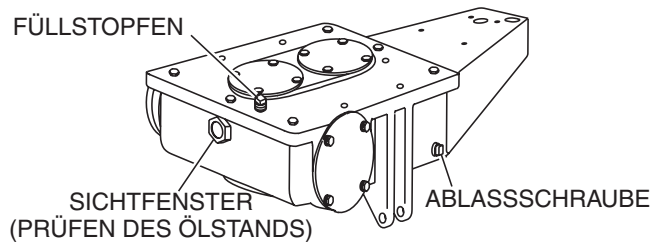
Füllstopfen / Sichtfenster des Getriebegehäuses
